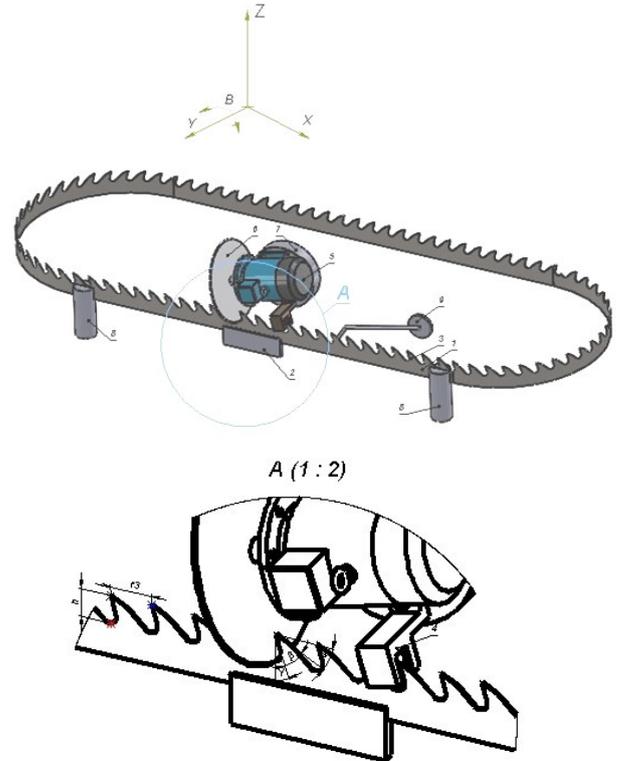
Схема процесса заточки зубьев ленточной пилы
